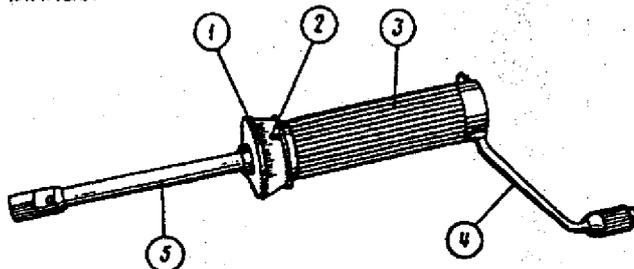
Chave dinamométrica 02.7812.9501: 1 - indicador móvel; 2 - indicador fixo; 3 - corpo; 4 - manivela; 5 - haste com encaixe para soquete.
